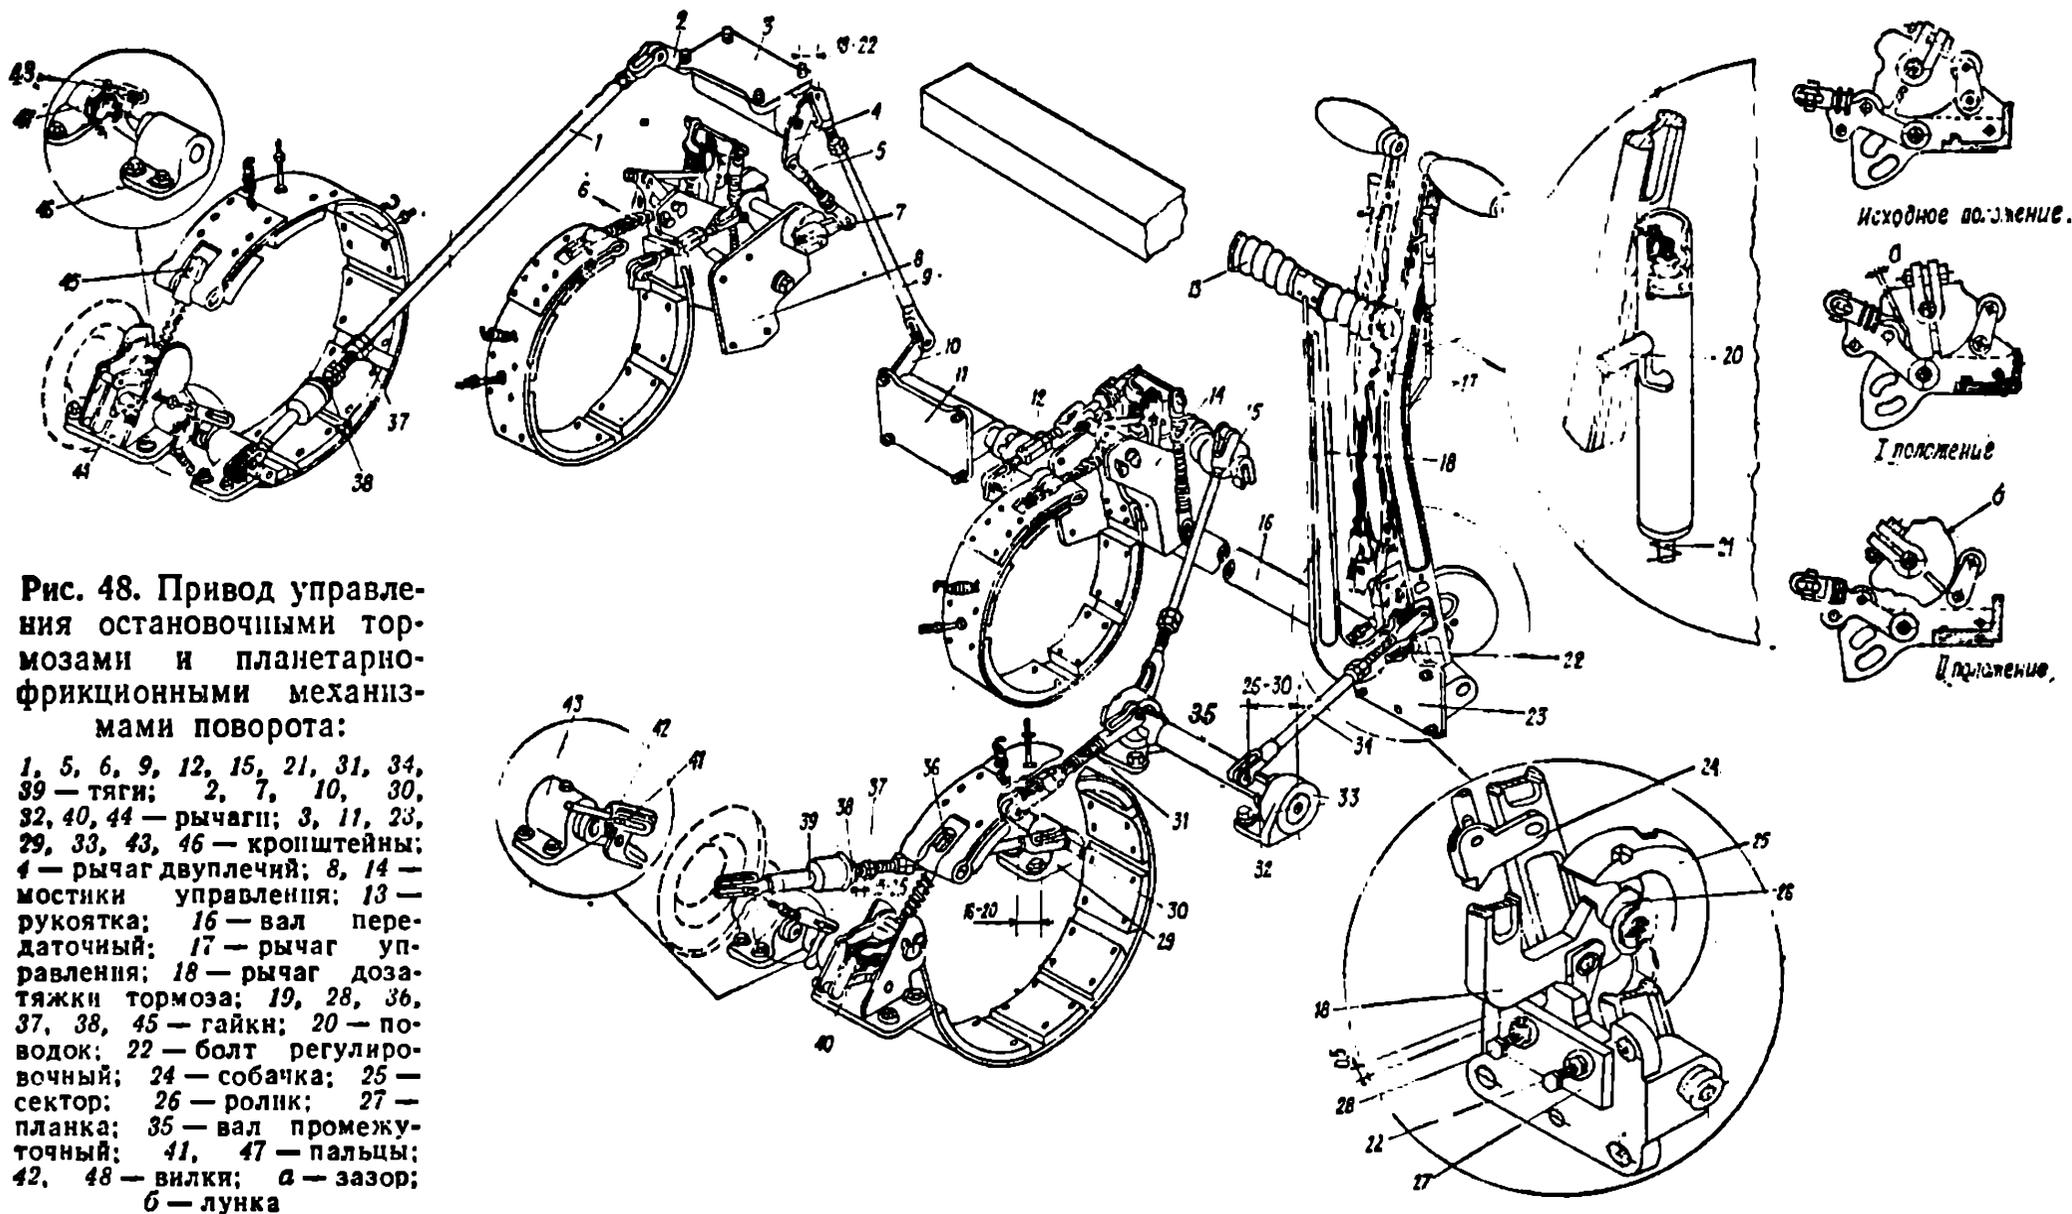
Привод управления остановочными тормозами и планетарно-фрикционными механизмами поворота:
